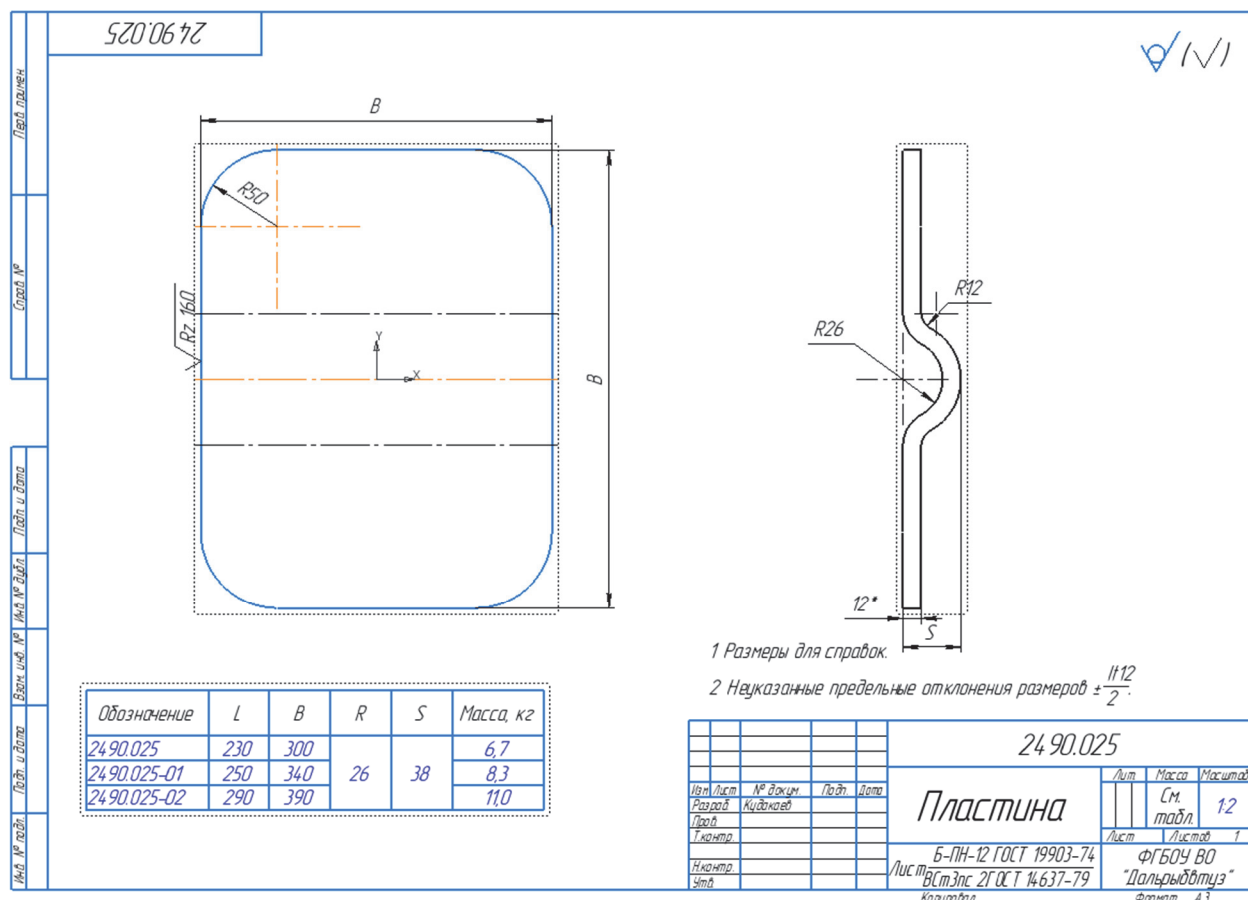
Чертёж детали «Пластина» в нескольких исполнениях
